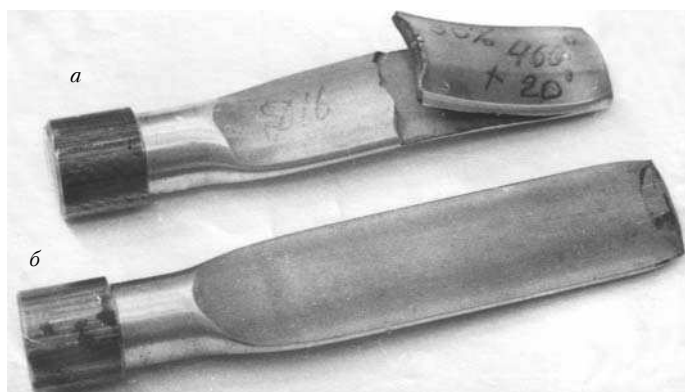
Вальцованные заготовки из сплава Д16, армированного нитевидными кристаллами SiC:
